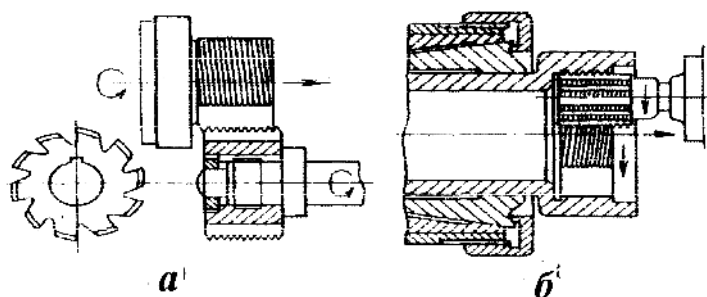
Схема нарезания резьбы гребенчатой фрезой: а - наружной; б - внутренней.
